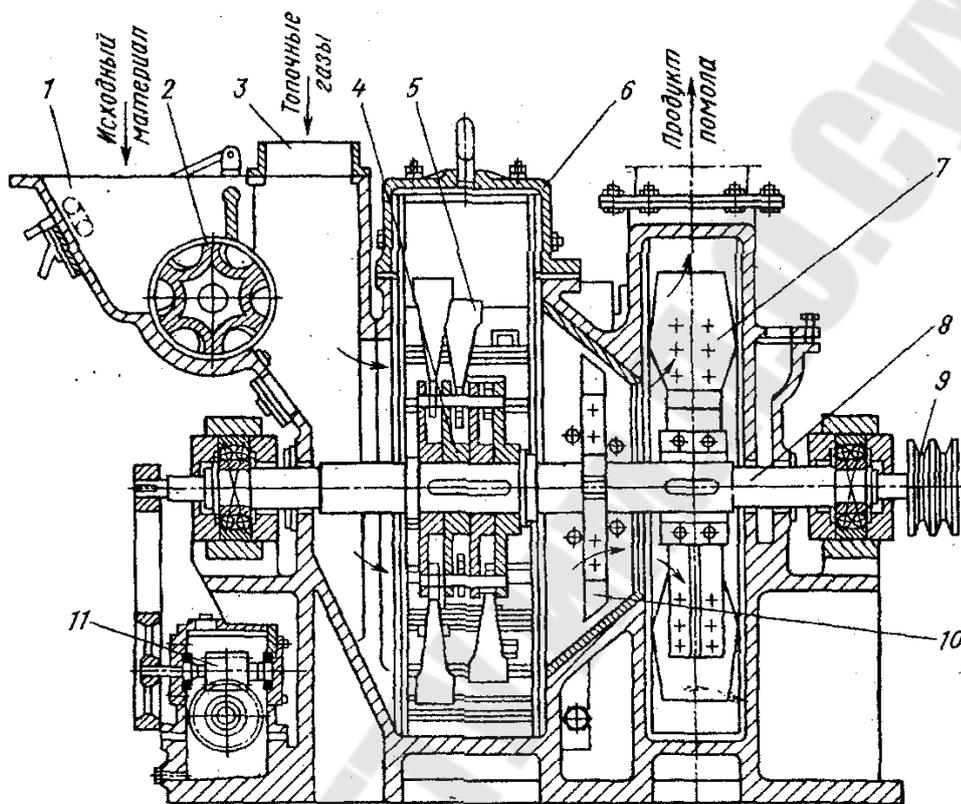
Молотковая мельница: 1- загрузочная воронка; 2- звездчатый питатель; 3- подвод воздуха и продуктов горения; 4- ротор; 5- молотки; 6- крестовина с ножами; 7- вентилятор; 8- выход аэросмеси; 9- вал; 10- ножи крестовины
